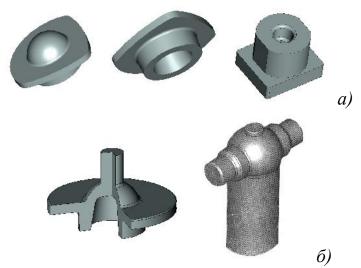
Поковка типа фланцев (а) и типа тройников (б)
